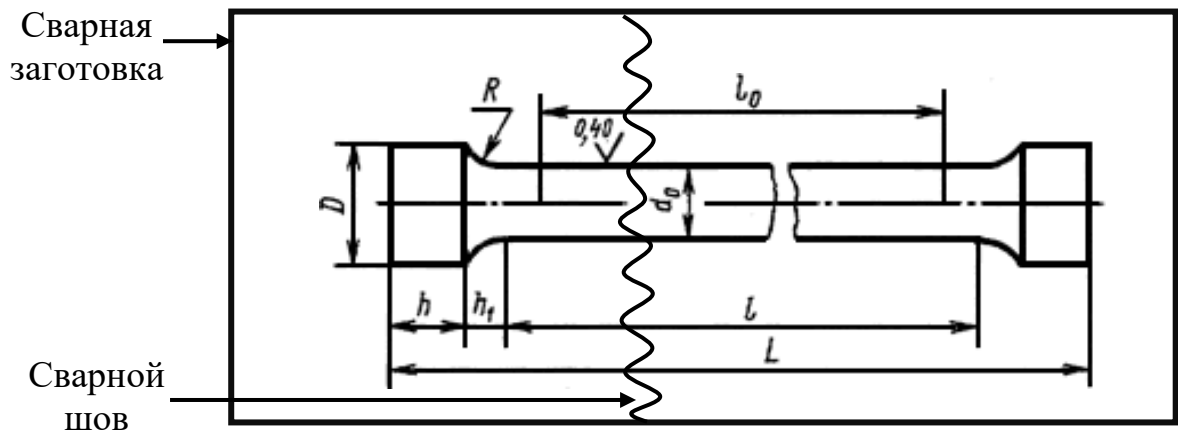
Схема вырезки образцов тип I по ГОСТ6996-66 из сварной заготовки.
